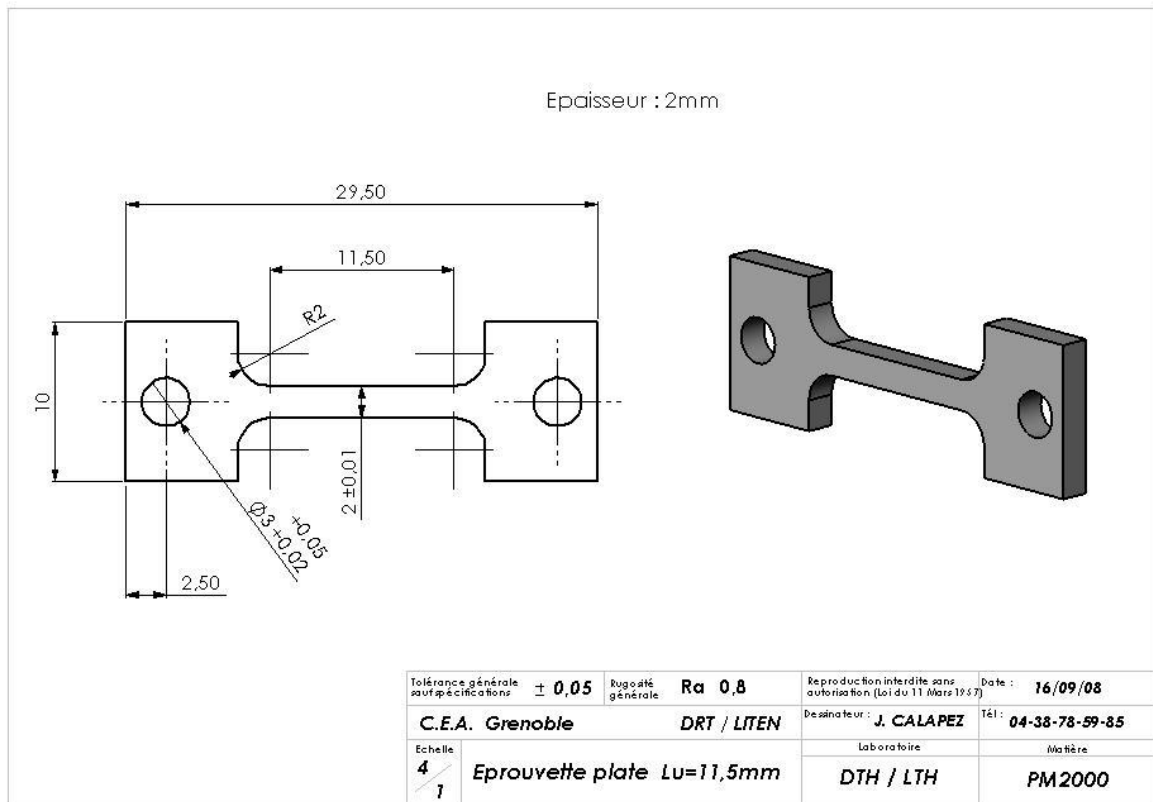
Epreuve section carrée 2 mm par 2 mm longueur utile 11.50 mm
